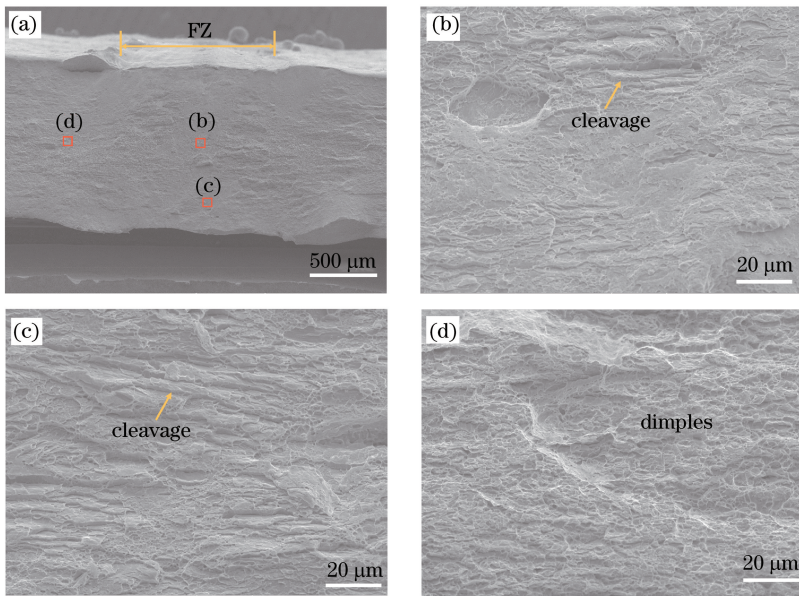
高速焊接试板在焊缝无偏移时的断口形貌。(a)宏观形貌;(b)焊缝中部;(c)焊缝下部,(d)热影响区
